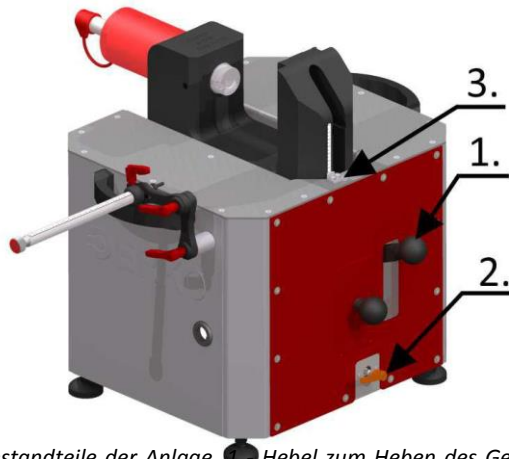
Bestandteile der Anlage, 1 – Hebel zum Heben des Gehäuses, 2 – Hebel zum Senken des Gehäuses, 3 – Anzeige der Gehäuseposition.
